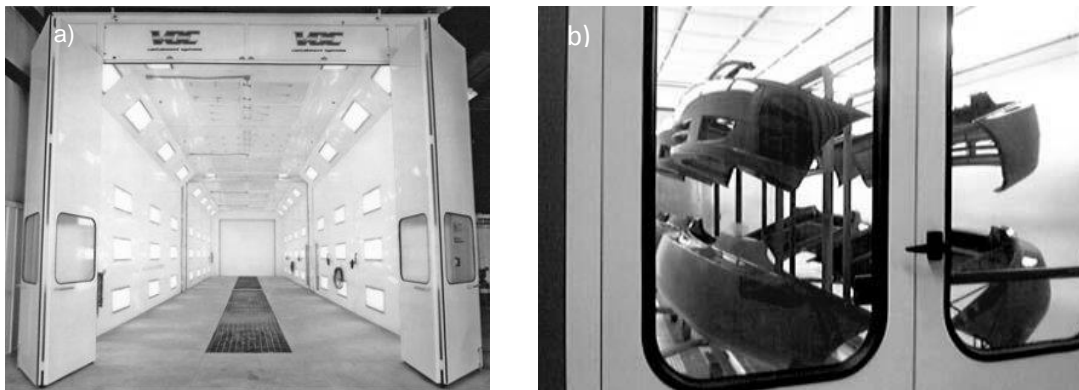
Horno, a) Cabina para hornear automóviles y b) Horneado de piezas automotrices [106].
